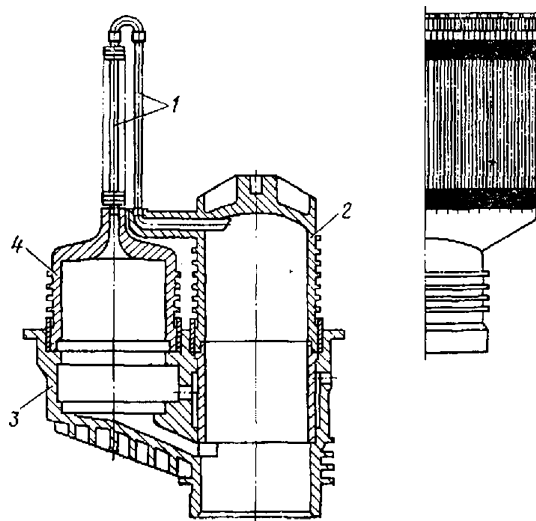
Нагревательная головка четырехцилиндрового двигателя Стирлинга двойного действия [4]:
